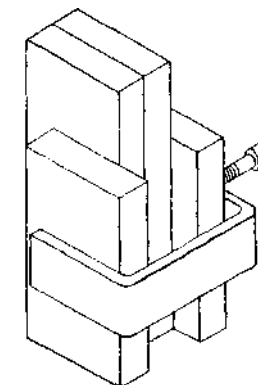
Спосіб кріплення заготовок для нарізання шипів
